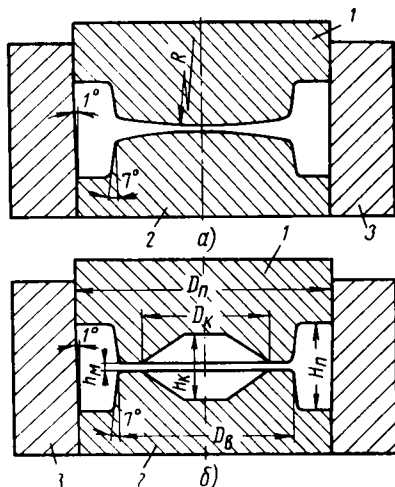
Лабораторные штампы для закрытой штамповки кольцевых поковок:
